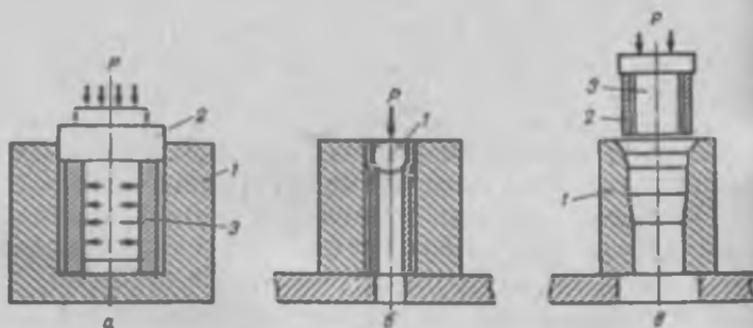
Способы ремонта деталей пластической деформацией:
